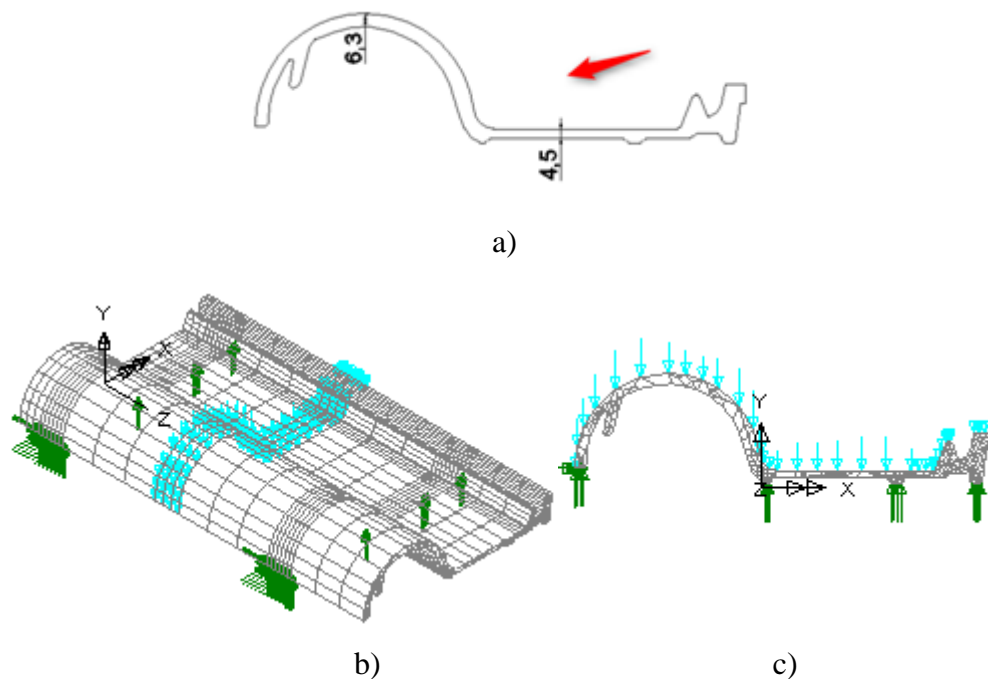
Modelo M2: a) perfil, b) perspectiva e c) vista frente.
